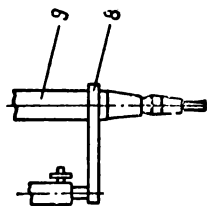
Циркуль-удлинитель типа ИЧ-12.
